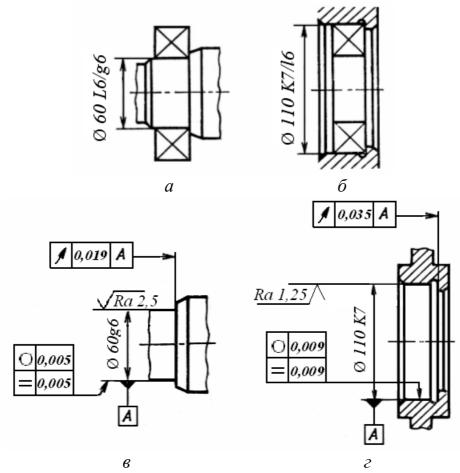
Эскиз сборочного узла с подшипниками качения и посадочных поверхностей вала и отверстия:
